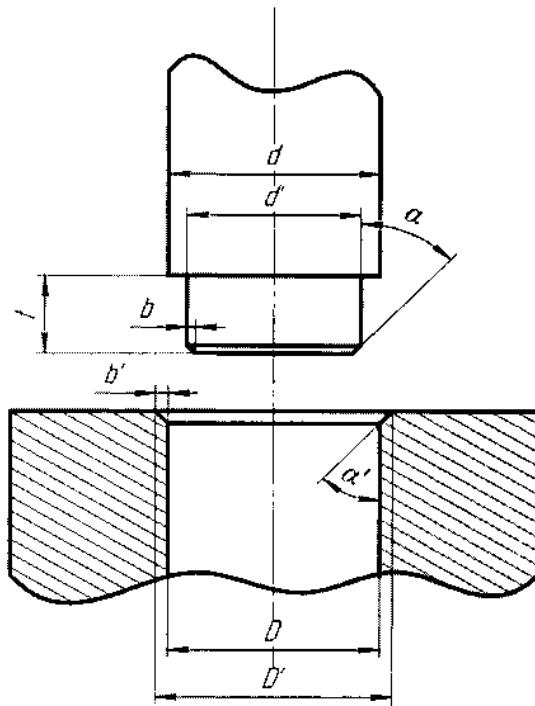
Геометрические параметры фасок и центрирующего уступа прессового сопряжения вал-втулка
